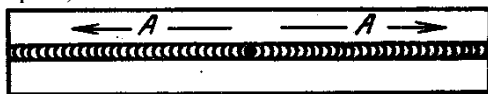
Сварка швов средней длины от середины к концам швам
